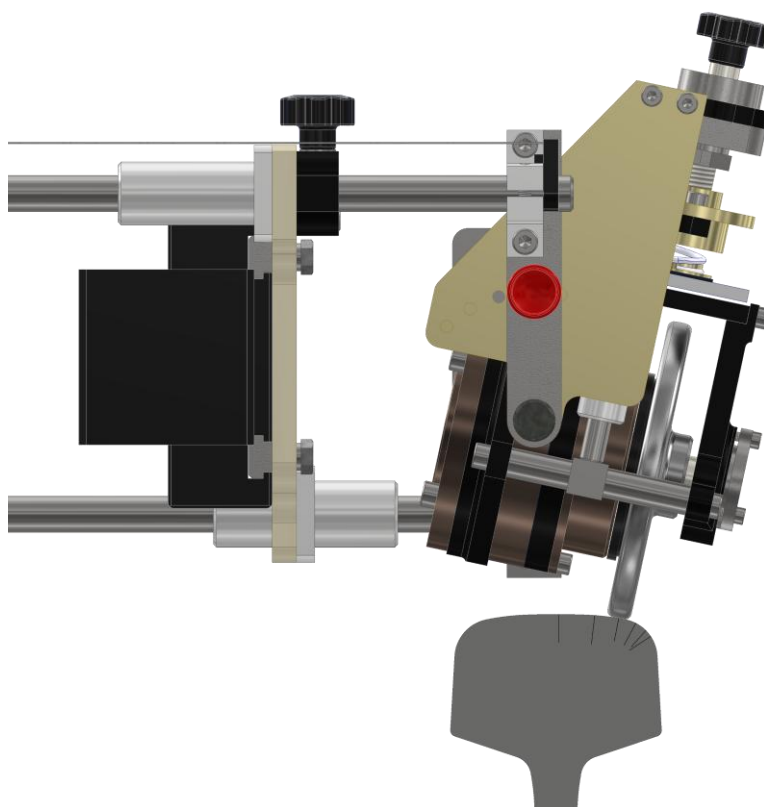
Napojení na horizontální pohonnou jednotku BUT Rail tribometru
